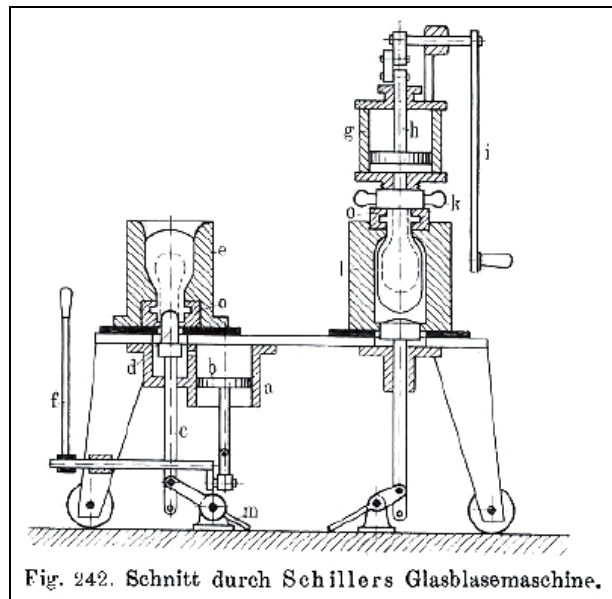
Schnitt durch Schillers Glasblasmaschine.
